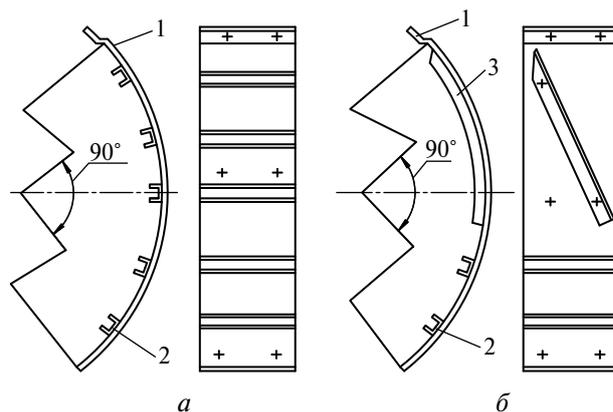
Глухие терочные поверхности приспособления ПСТР-10В: а — с домолачивающими; б — с винтовыми направляющими; 1 — щит; 2 — домолачивающая планка; 3 — винтовой направлятель
